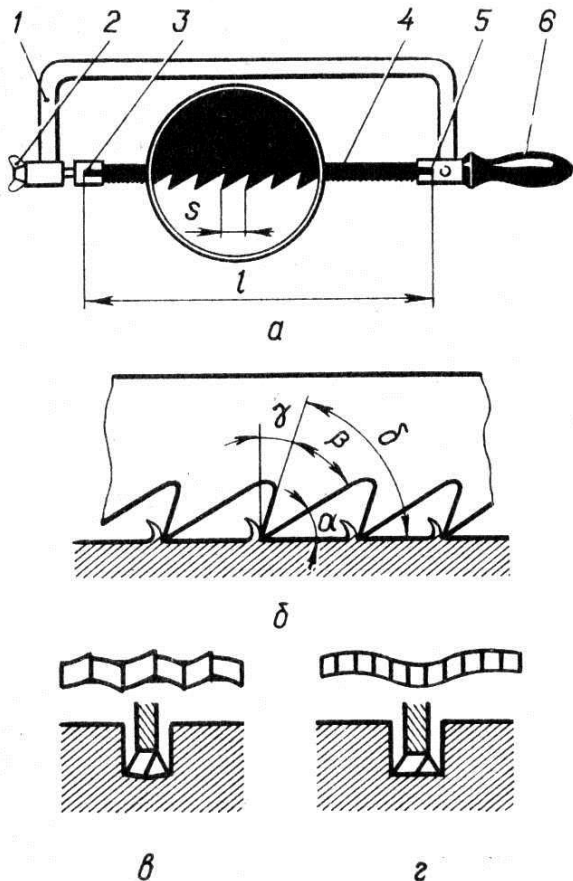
Ручная ножовка а – устройство, б - углы заточки, в – разводка зубьев «по зубу», г – разводка зубьев «по полотну».
